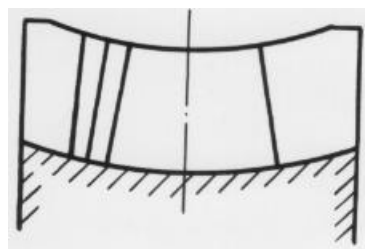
Розташування контактних ліній на поверхні зуба колеса.
